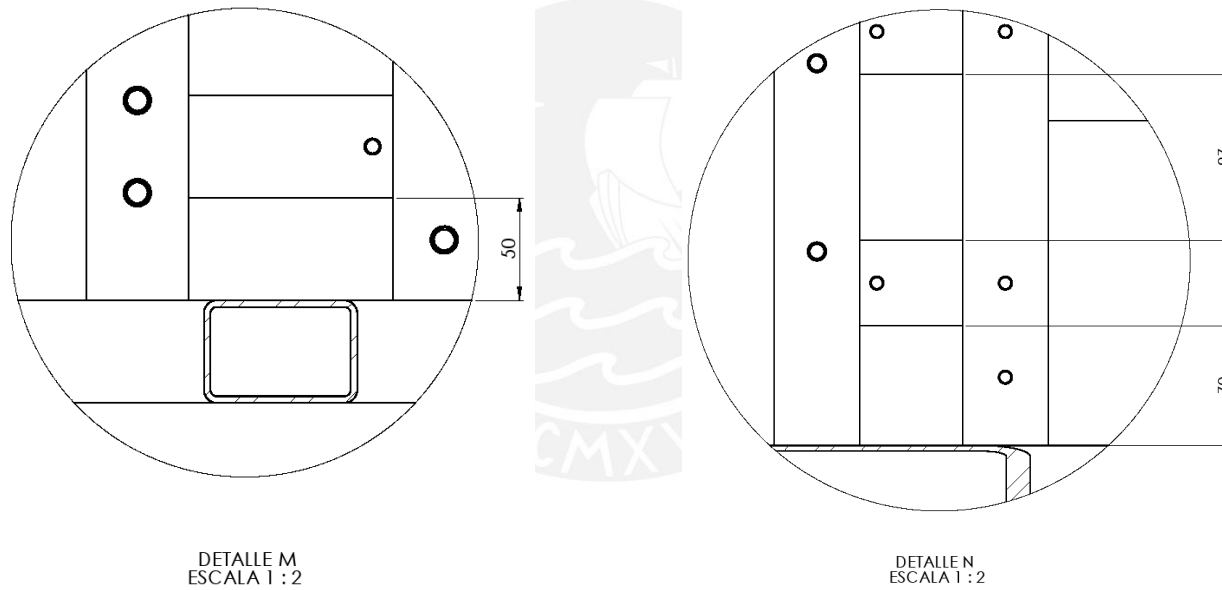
Vistas de detalles M y N de la estructura del sistema mecatrónico. Fuente: Elaboración propia.
